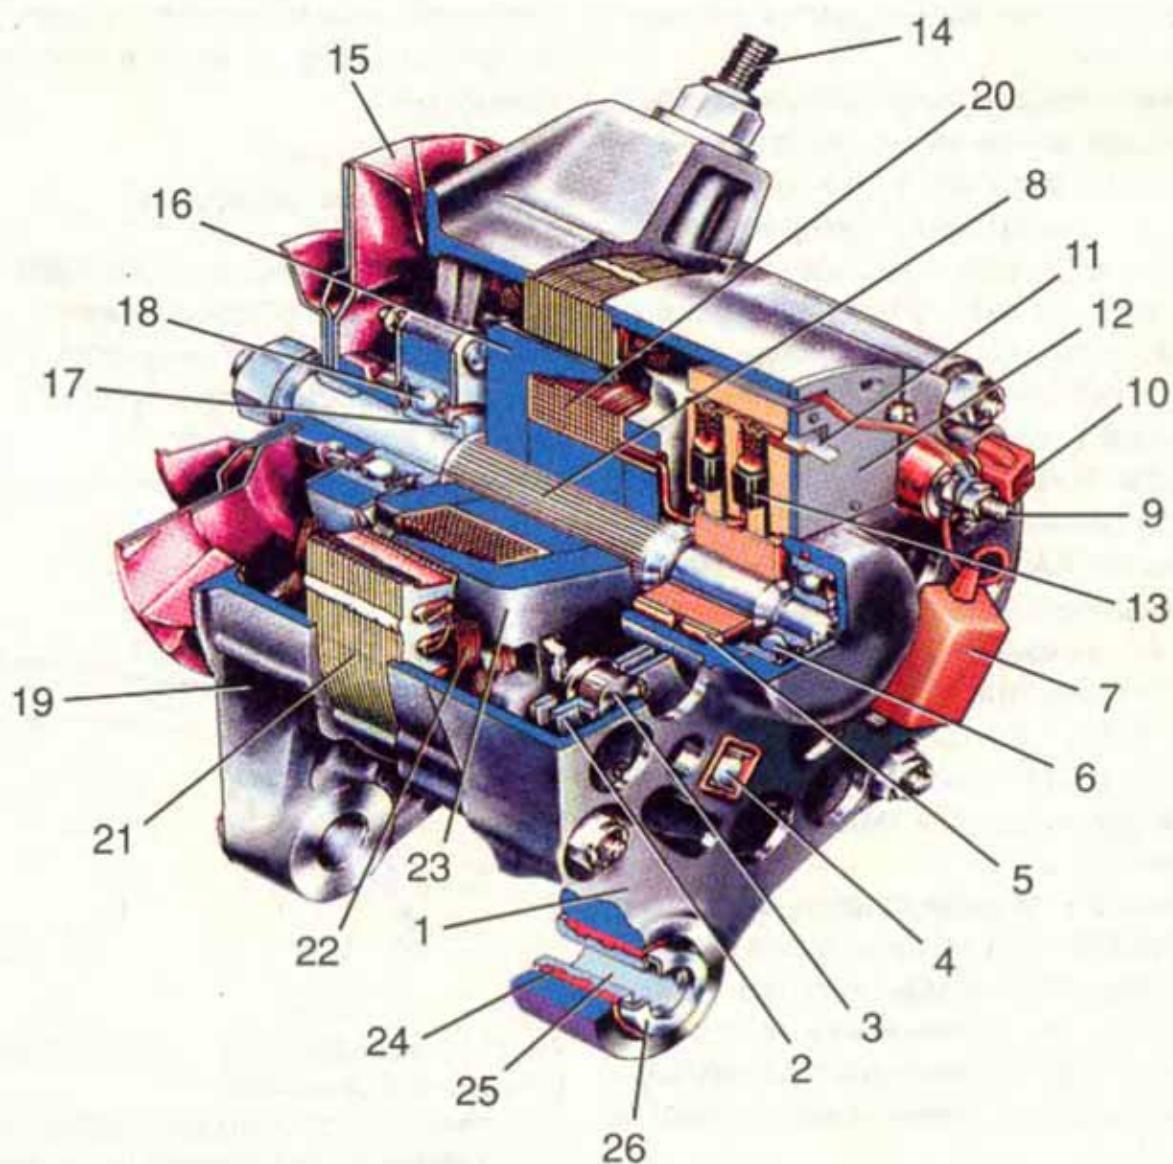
Устройство генератора 37.3701: 1 — крышка со стороны контактных колец; 2 — выпрямительный блок; 3 — диод выпрямительного блока; 4 — винт крепления выпрямительного блока; 5 — контактное кольцо; 6 — задний шарикоподшипник; 7 — конденсатор; 8 — вал ротора; 9 — вывод "30" генератора; 10 — вывод обмотки возбуждения генератора; 11 — вывод регулятора напряжения; 12 — регулятор напряжения; 13 — щетка; 14 — шпилька крепления генератора к натяжной планке; 15 — шкив с вентилятором; 16 — полюсной наконечник ротора; 17 — дистанционная втулка; 18 — передний шарикоподшипник; 19 — крышка со стороны привода; 20 — обмотка ротора; 21 — статор; 22 — обмотка статора; 23 — полюсной наконечник ротора; 24 — буферная втулка; 25 — втулка; 26 — подвижная втулка.
